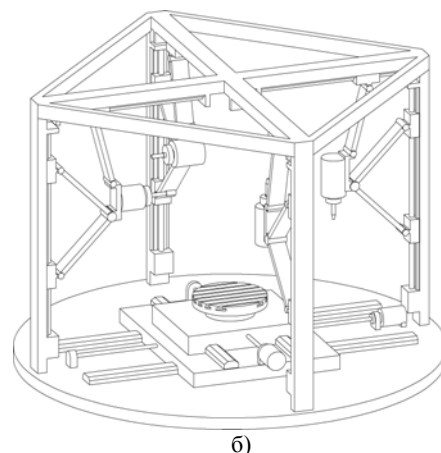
Двошпиндельна компоновка свердильно-фрезерного верстату з модулем повороту шпинделя на рухомій платформі
